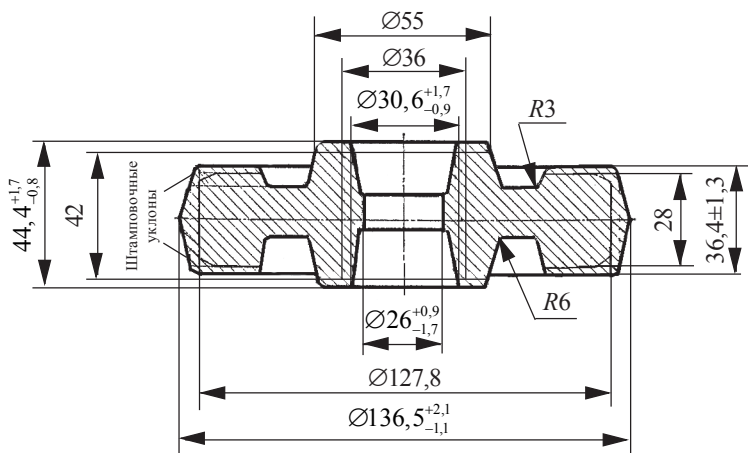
Чертеж штамповки шестерни (основные размеры)
